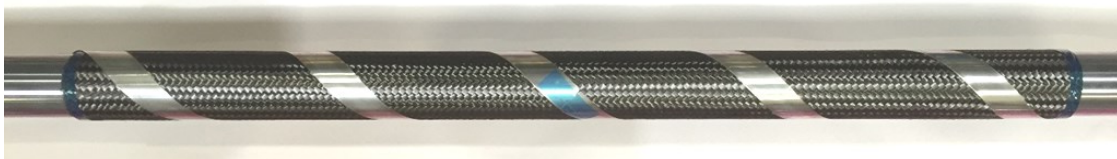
Lückenhafte Geflechtpreform umwickelt mit Druckblech
